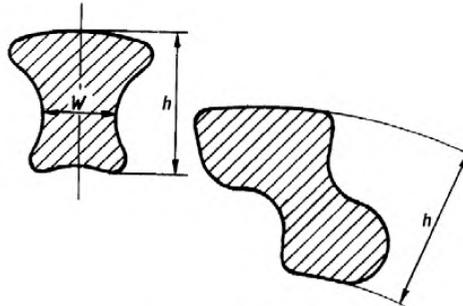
Сечения проволоки полностью закрытой и полузакрытой конструкций
